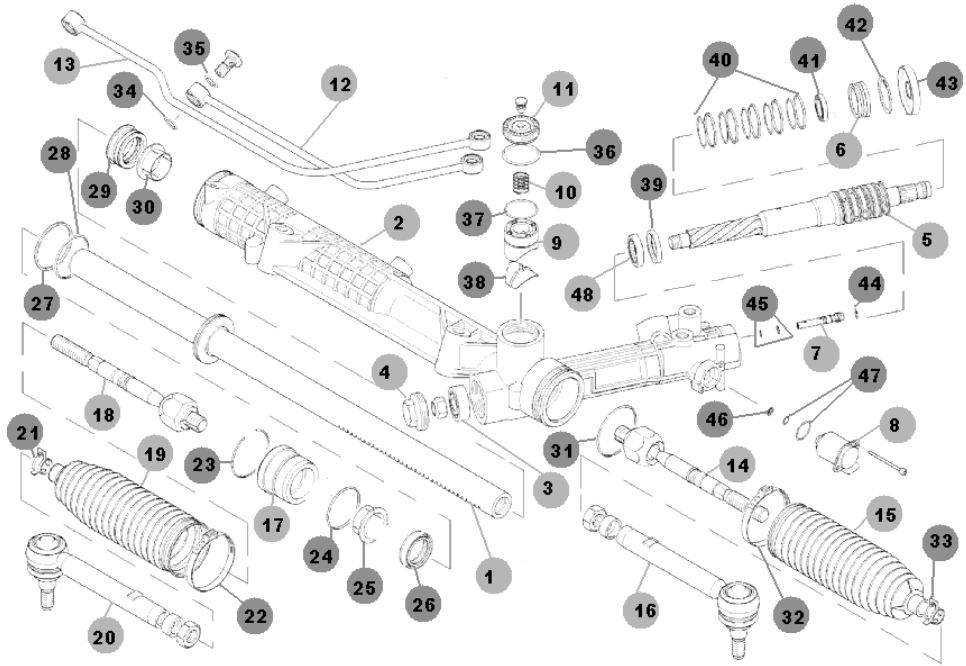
Пристрій рульової рейки з серватроніком 1-й вигляд
